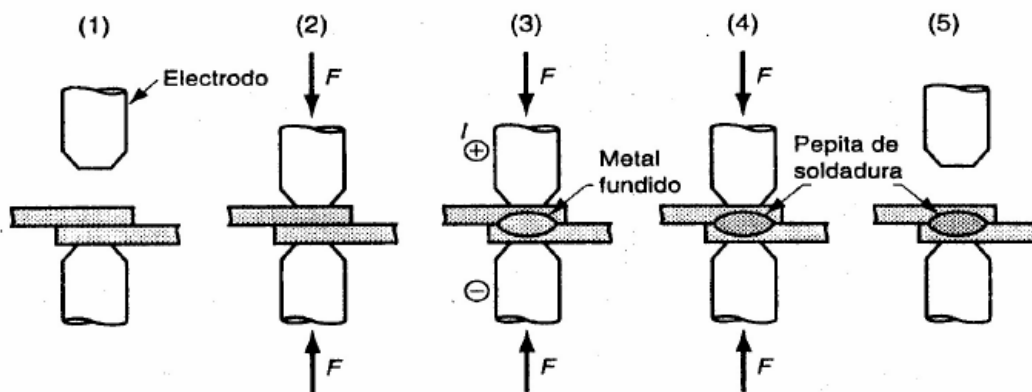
Pasos en un ciclo de soldadura de puntos.
